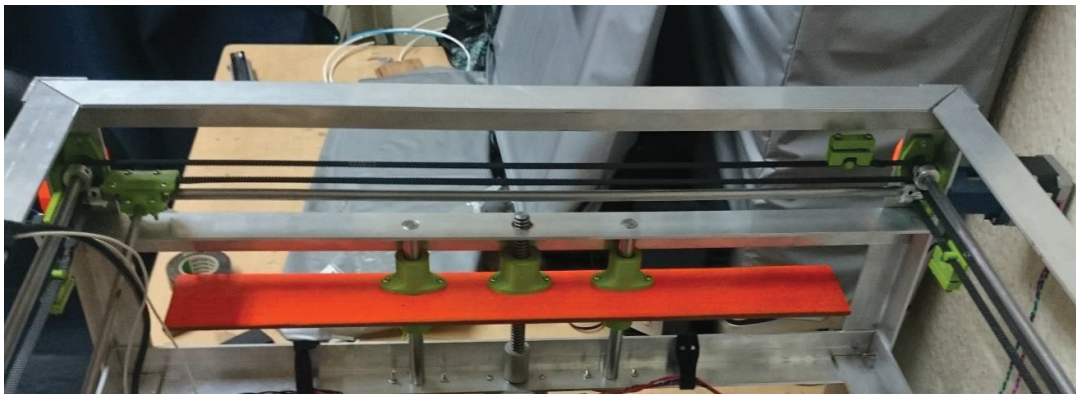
Fotografía de las bandas y sensores montados en el equipo.
